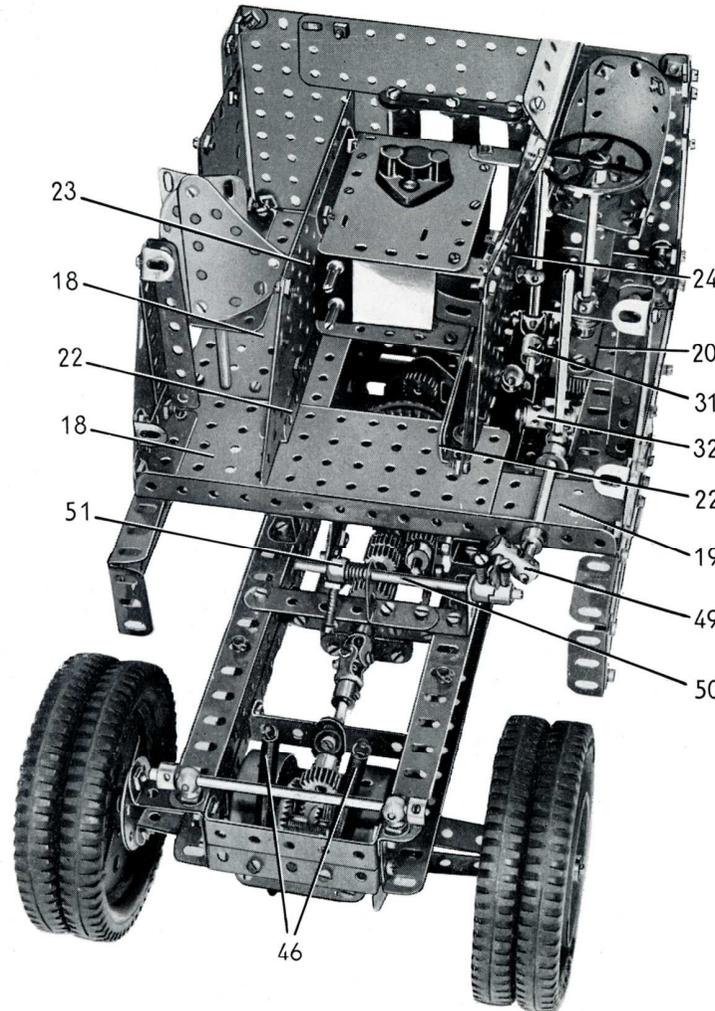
Vue en bout du basculeur automoteur, la benne et le devant de la carrosserie ont été enlevés pour montrer comment est monté le moteur électrique universel.
